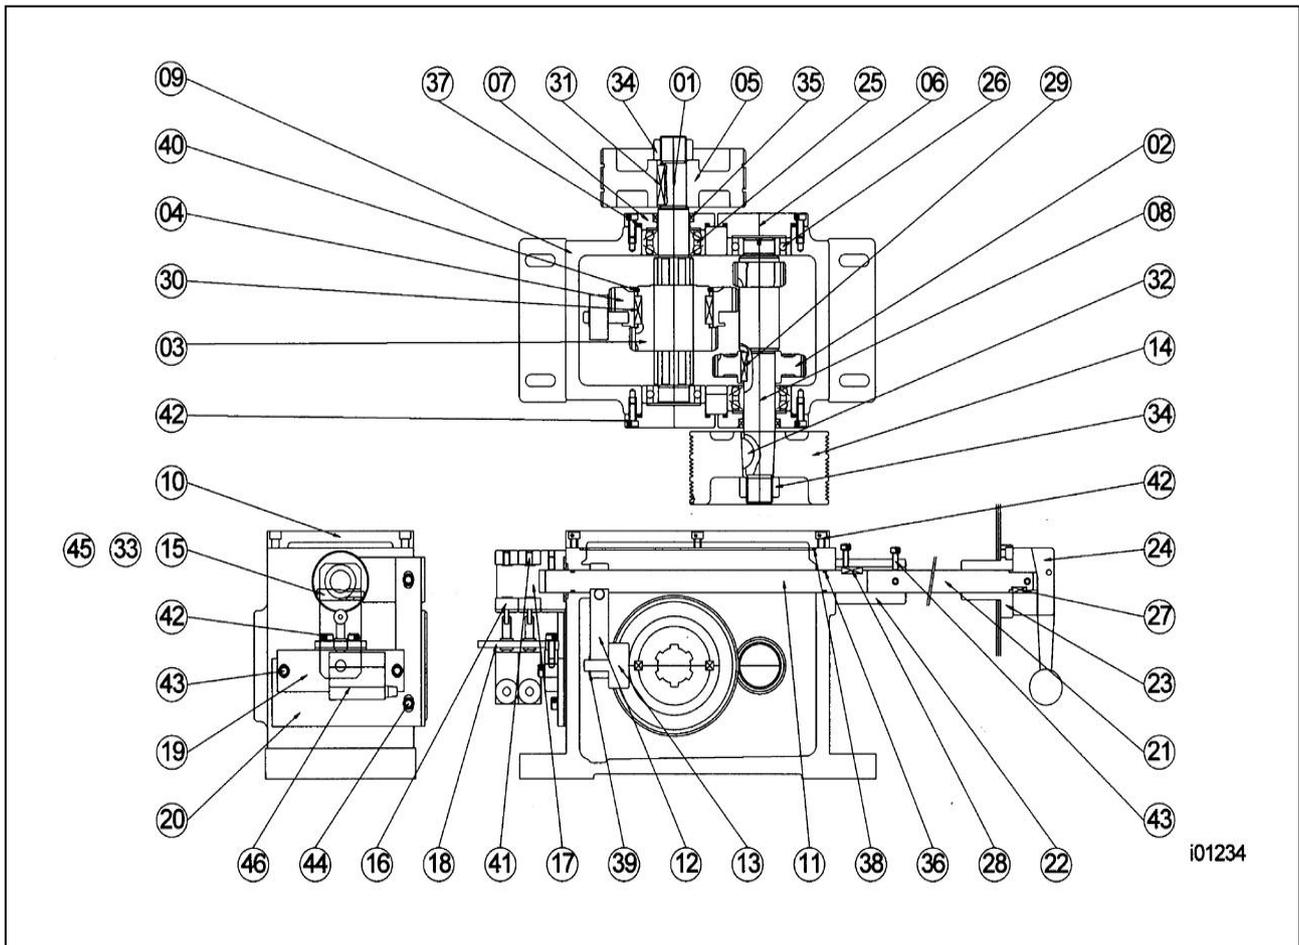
Baugruppe Drehzahlwähler der Maschine SLX 355
